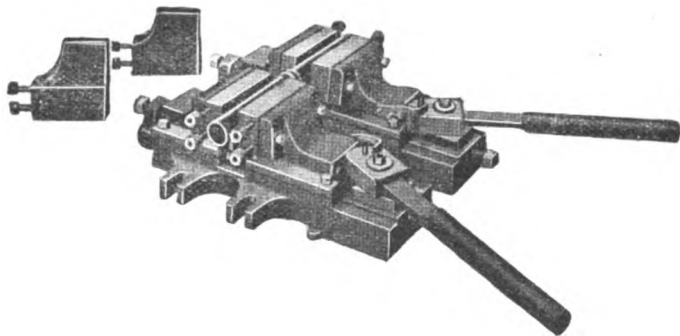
Macchina per la saldatura elettrica. Sistema Thomson.
